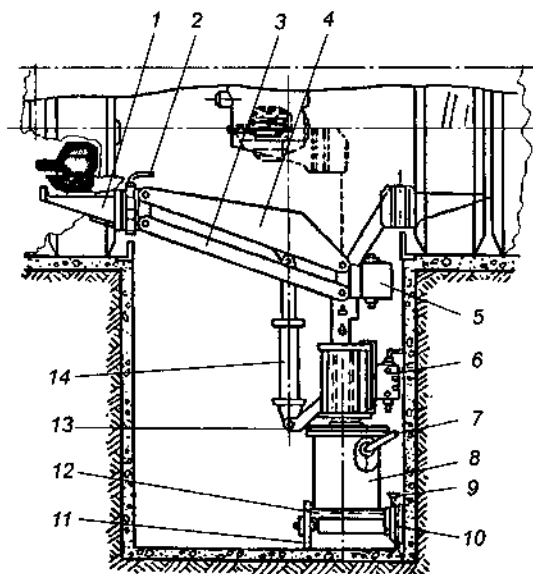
Устройство для замены агрегатов автомобиля: 1 — сменный подхват; 2 — соединительная ручка; 3 — пантограф; 4 — подъемная стрела; 5 — бачок; 6 — золотник; 7 — воздухораспределительный кран; 8 — пневмоцилиндр; 9 — двутавровая балка; 10 — металлическое колесо; 11 — обрешиненное колесо; 12 — тележка; 13 — кронштейн; 14 — гидроцилиндр
